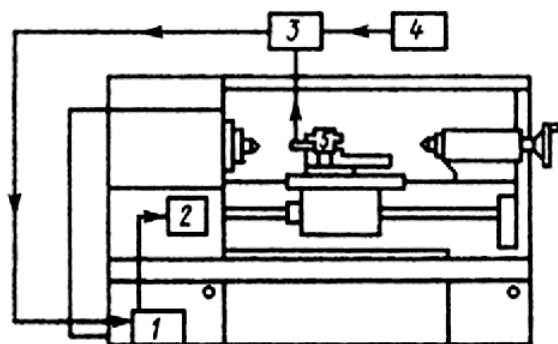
Токарный станок с системой адаптивного управления:
